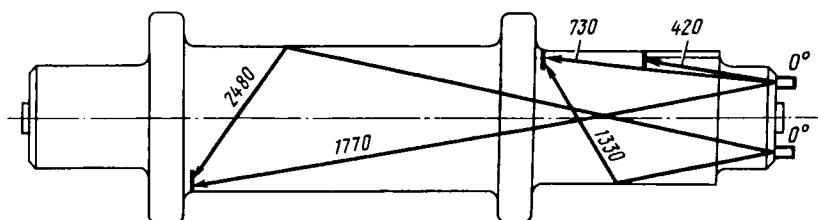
Схемы и зоны контроля прямым искателем со стороны правого торца главного приводного вала эскалатора Н-40М
